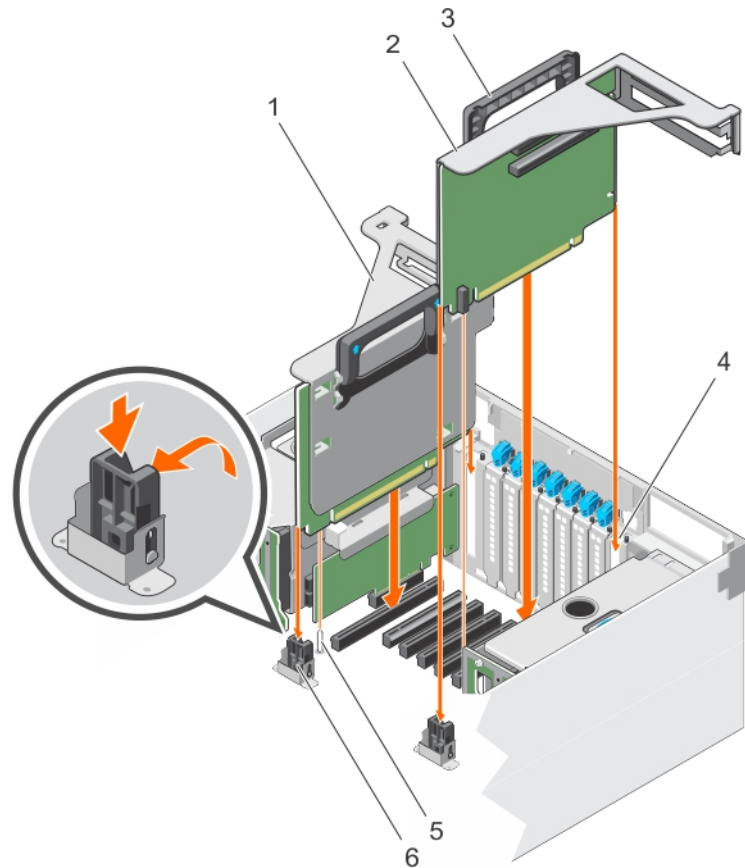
Installation de la carte de montage pour carte d'extension gauche ou droite
